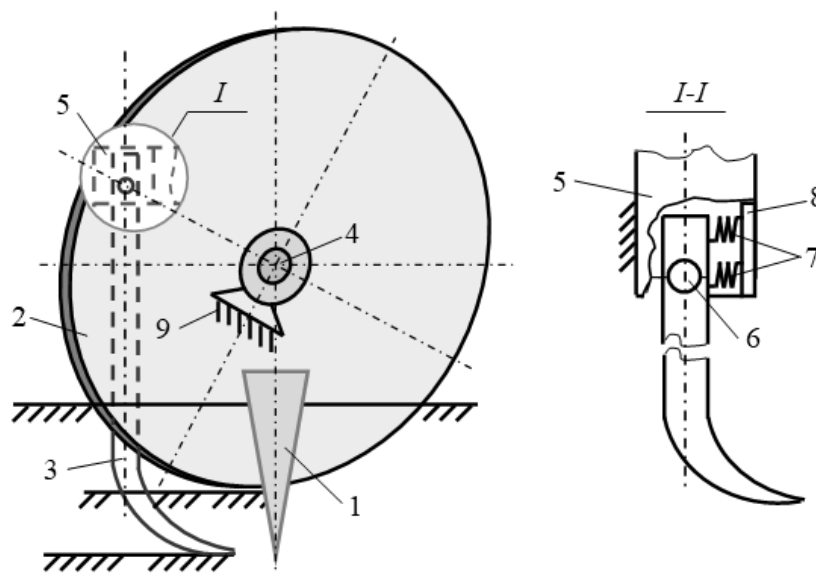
Конструктивна схема комбінованого копача: 1 – коренеплід; 2 – сферичний диск; 3 – розрихлювач; 4 – вісь обертання диска; 5 – кронштейн кріплення розрихлювача; 6 – вісь повороту розрихлювача; 7 – пружина; 8 – упорна пластина; 9 – рама
